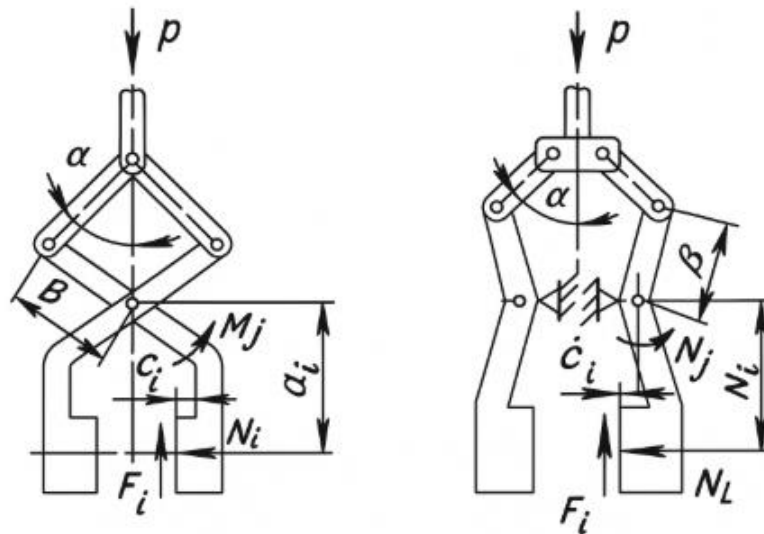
Важільна схема приводу механічного захоплювача
